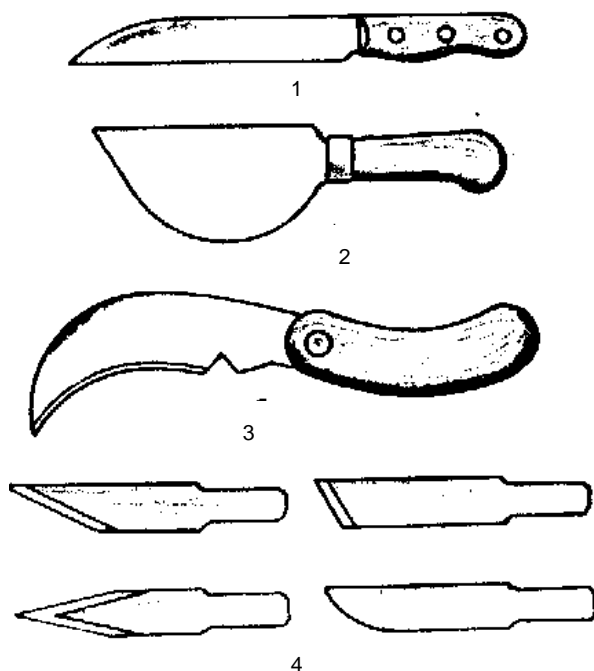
Виды рабочих ножей корзиноплетельщика:
